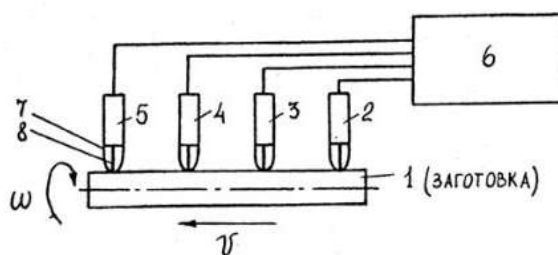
Схема способа нагрева заготовок перед штамповкой низкотемпературной плазмой (факельным разрядом)
